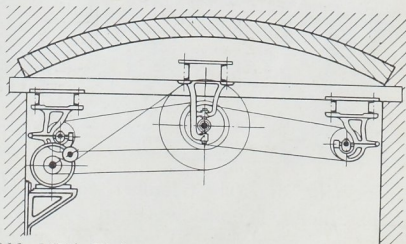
Einbau eines Triebwerks unter einem Gewölbe.
